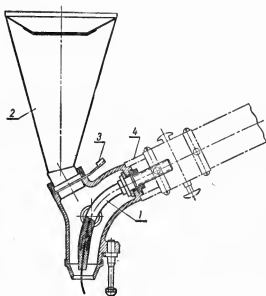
Держатель ДШ-5 шлангового полуавтомата ПШ-5:
